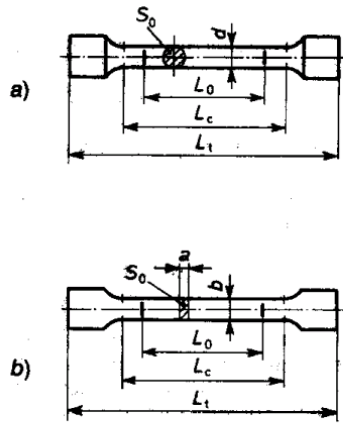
Provini per prove di trazione: a) sezione circolare; b) sezione rettangolare
